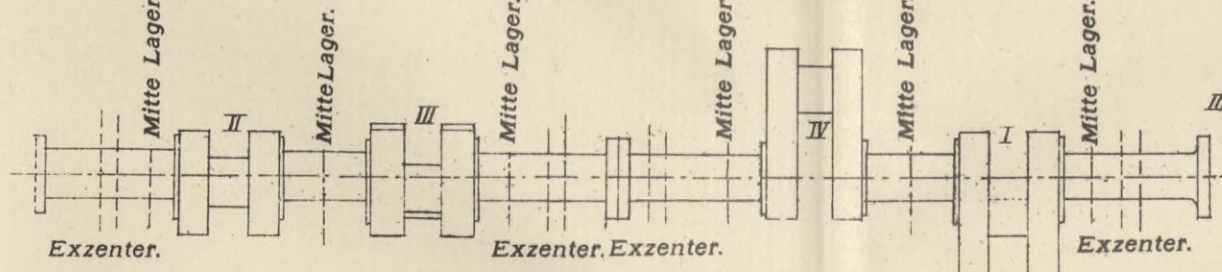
Kurbelwelle einer Vierfach-Expansionsmaschine.
